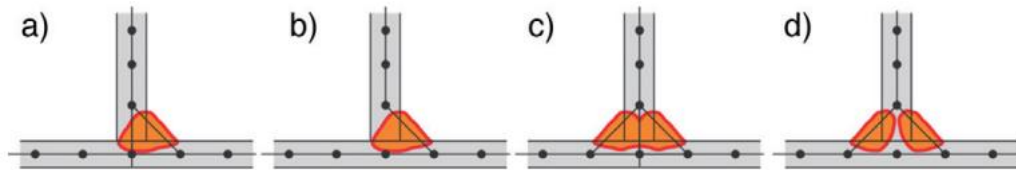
Representação numérica da penetração de solda. (a) Penetração total com solda assimétrica. (b) Penetração parcial com solda assimétrica. (c) Penetração total com solda simétrica. (d) Penetração parcial com solda simétrica [Silveira, Mezzomo e Goedel, 2017].
